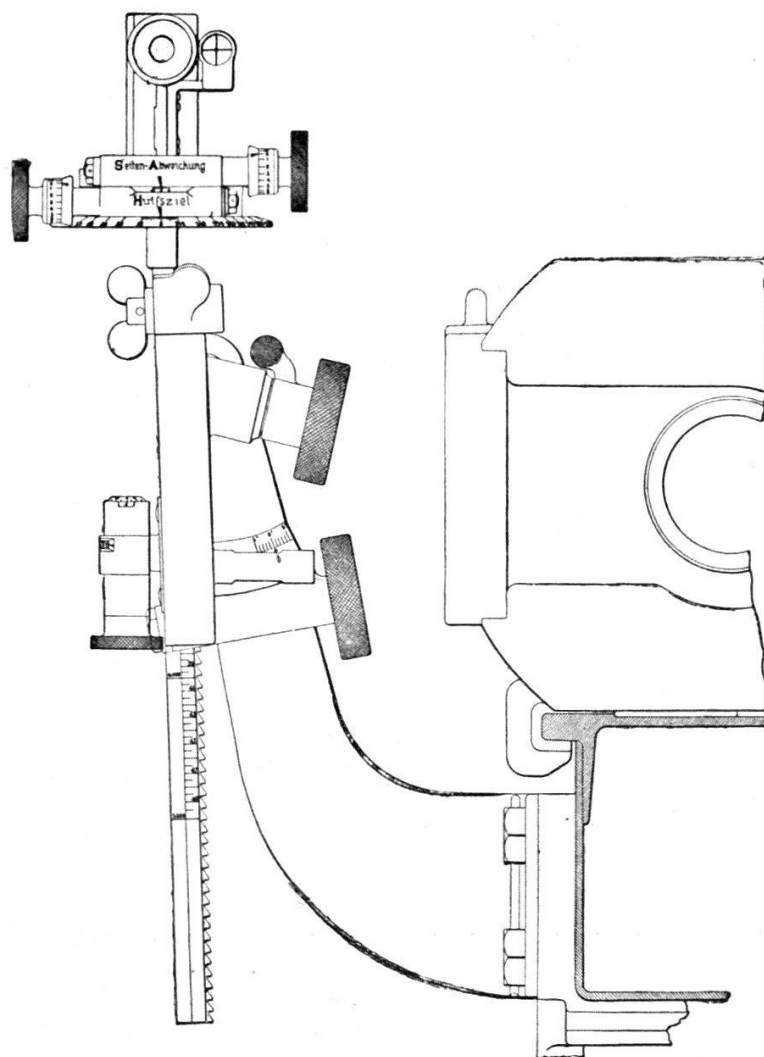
Hausse à lunette système Krupp. Assemblage sur le berceau d'une pièce à recul sur l'affût.
